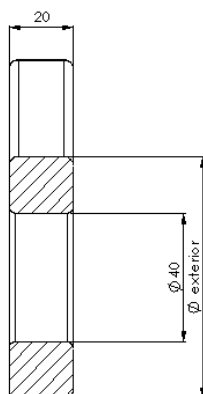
Croquis de la sección resistente a tracción (I)
